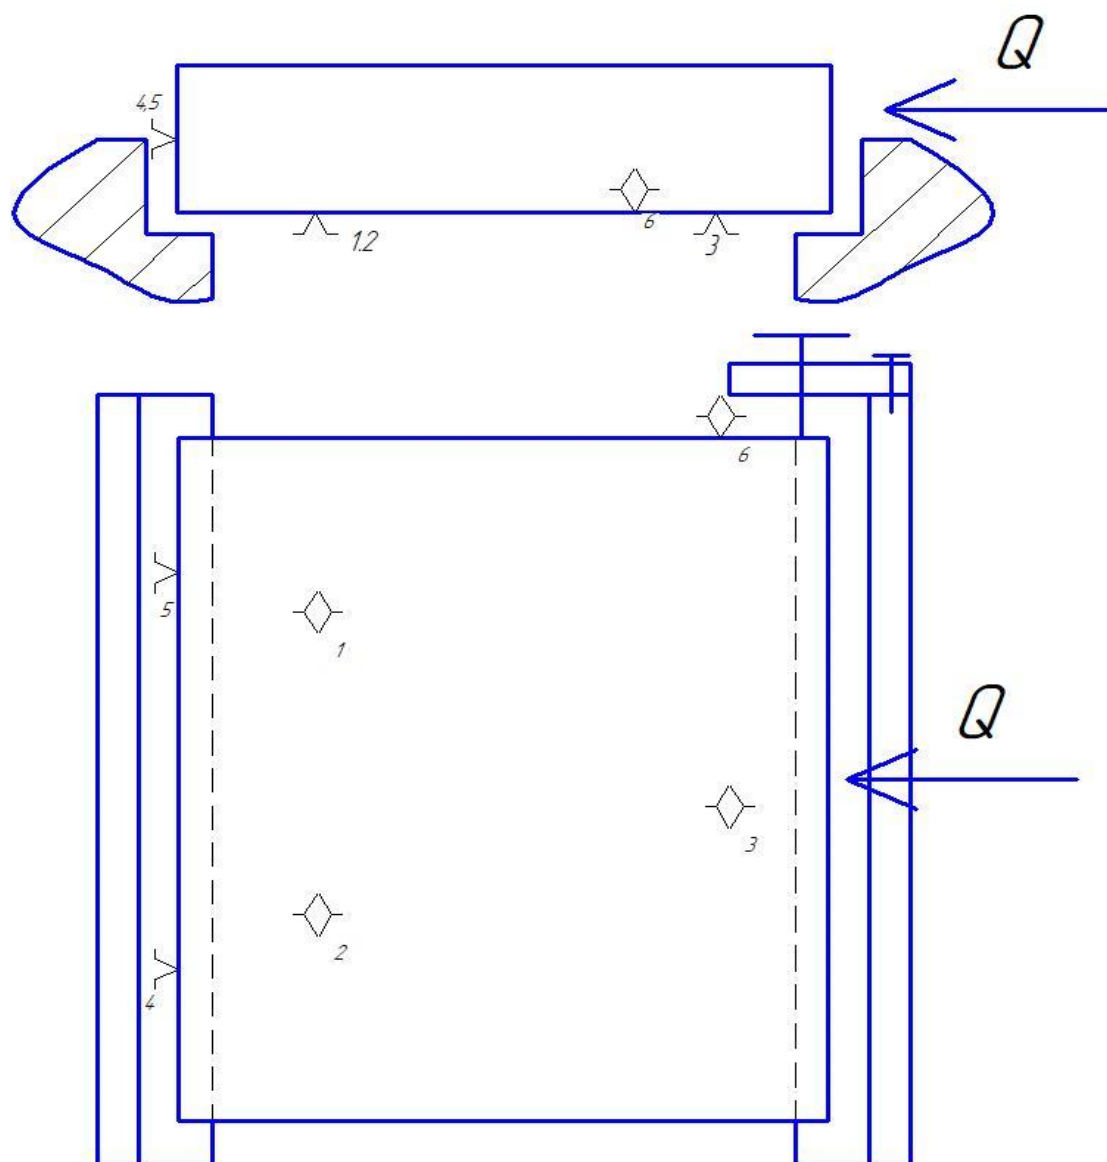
Принципиальная схема зажима заготовки в приспособлении с указанием мест приложения силы зажима.
